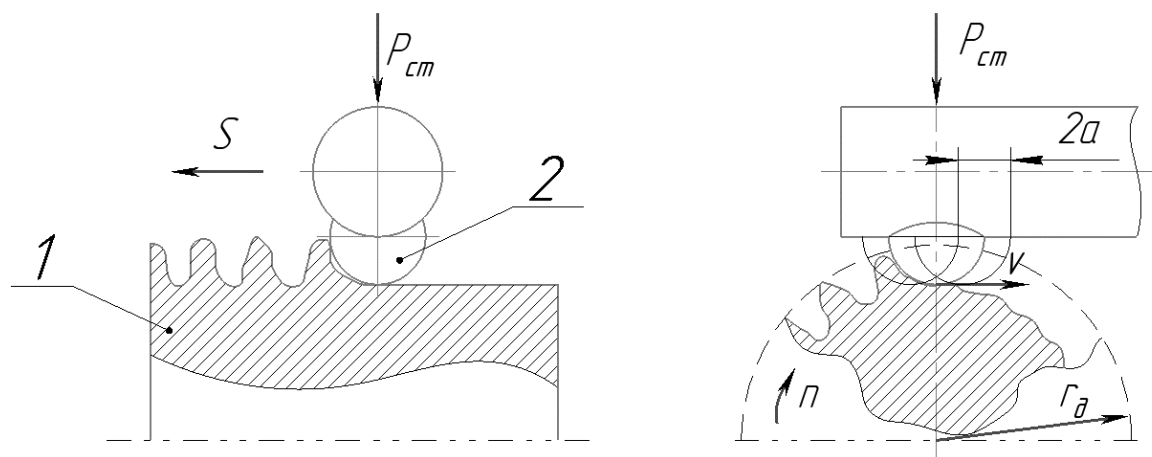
Схема введения колебаний по касательной к поверхности:
